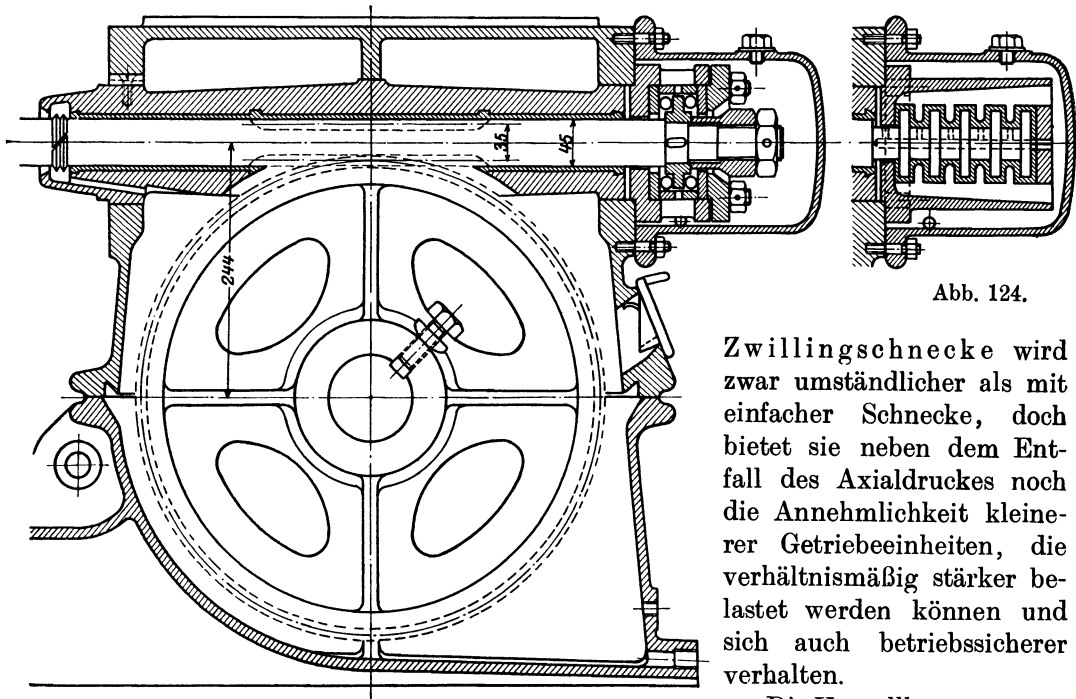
Ausführung der Maschinenfabrik Carl Flohr, Berlin.
